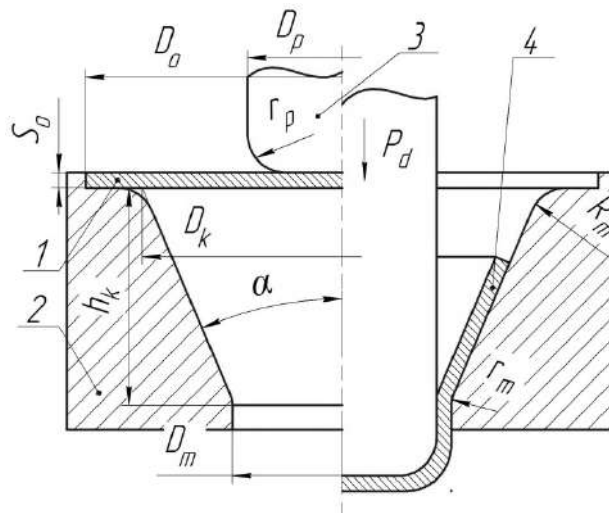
Схема комбінованого витягування в одноконусній матриці
